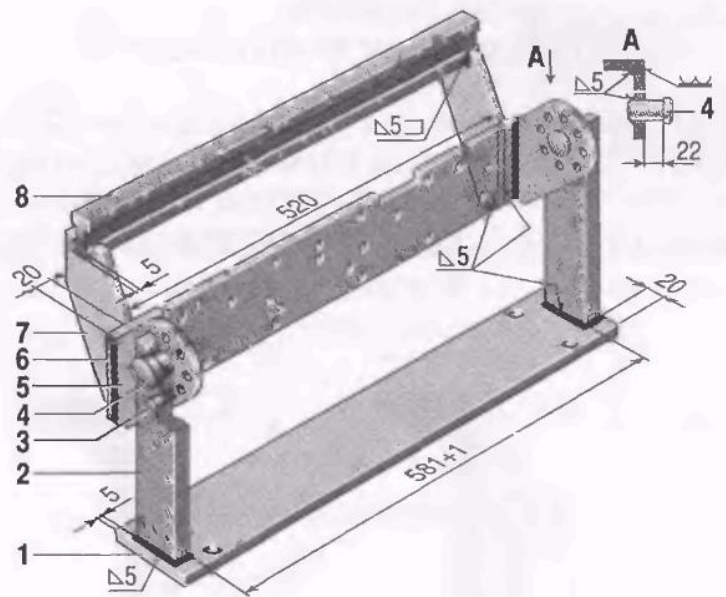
Принципова схема універсального стелу оригнальної конструкції для облугування і ремонту головок блоків цилндрів: 1 - основа; 2 - стійка (2 шт.); 3 - стопорний гвинт (2 шт.); 4 - цафа (2 шт.); 5 - пластина (2 шт.); 6 - несуча пластина; 7 - опора напрямної (2 шт.); 8 – напрямна.
